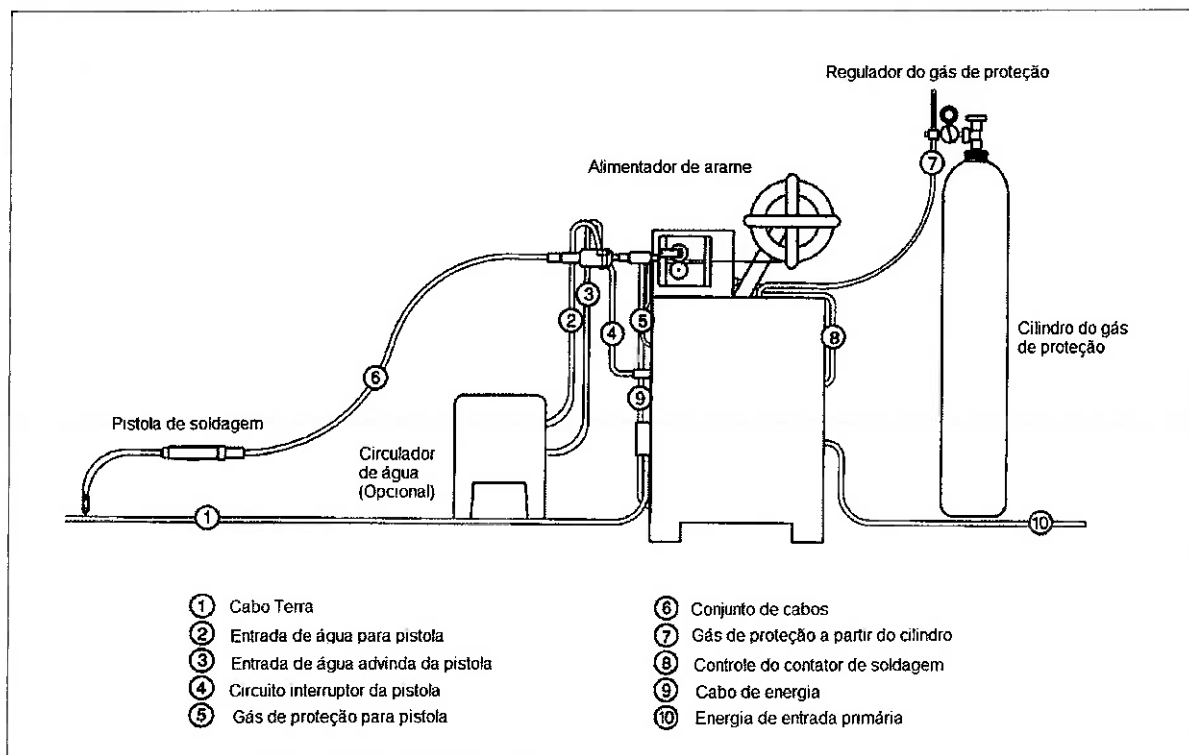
Esquema do equipamento de soldagem MIG/MAG [15]
